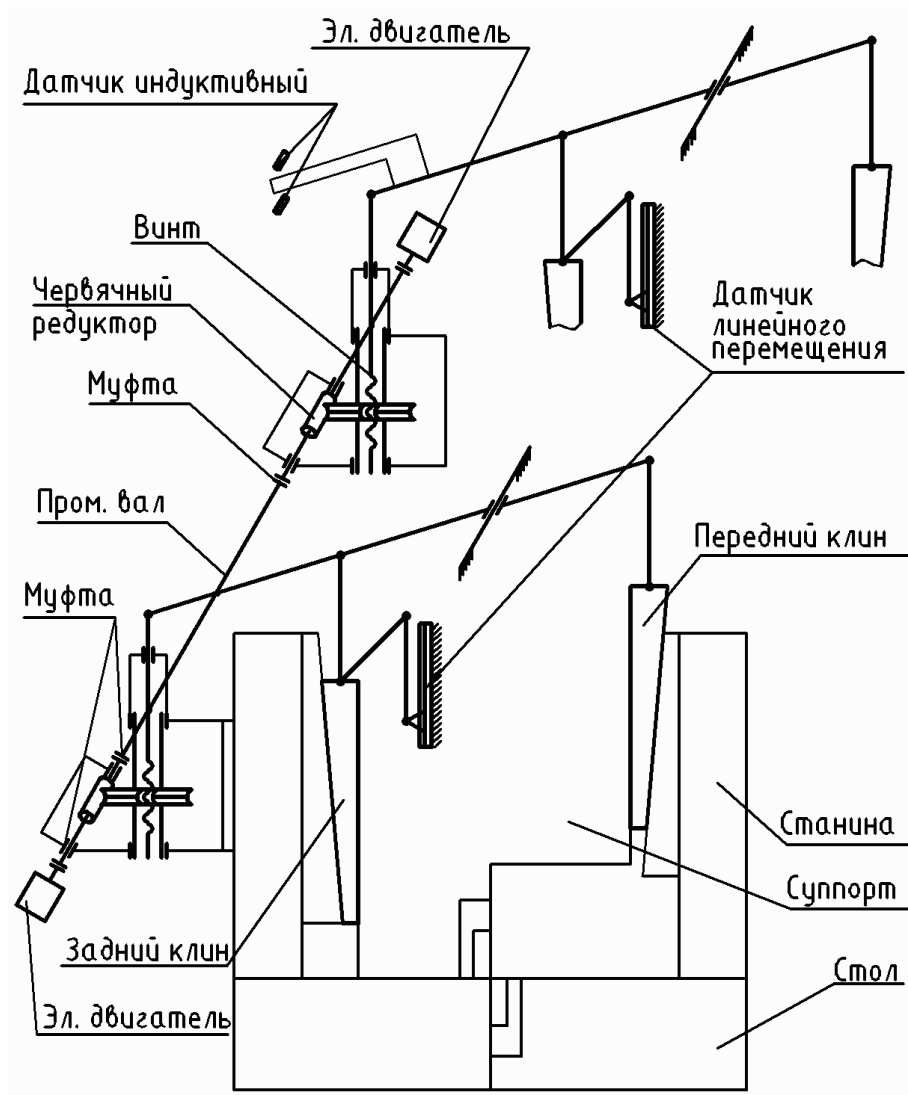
Кинематическая схема устройства регулировки бокового зазора.
